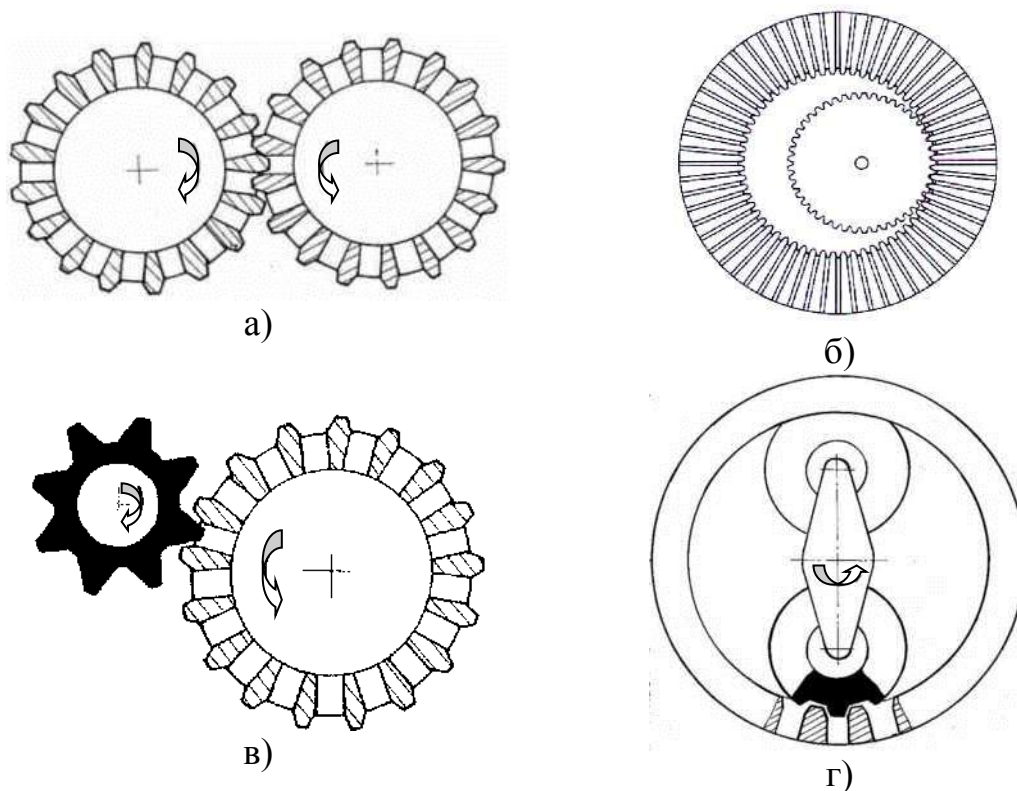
Схеми робочих органів шестеренних пресів [10]: а – з двома рівновеликими колесами-матрицями; б – матриця і внутрішній пресуючий валець; в – велике колесо-матриця і мале пресувальне колесо по зовнішньому зачепленню; г – матриця і кілька внутрішніх пресуючи вальців
